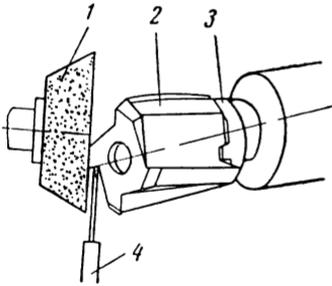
Схема заточки насадного зенкера по задней поверхности
